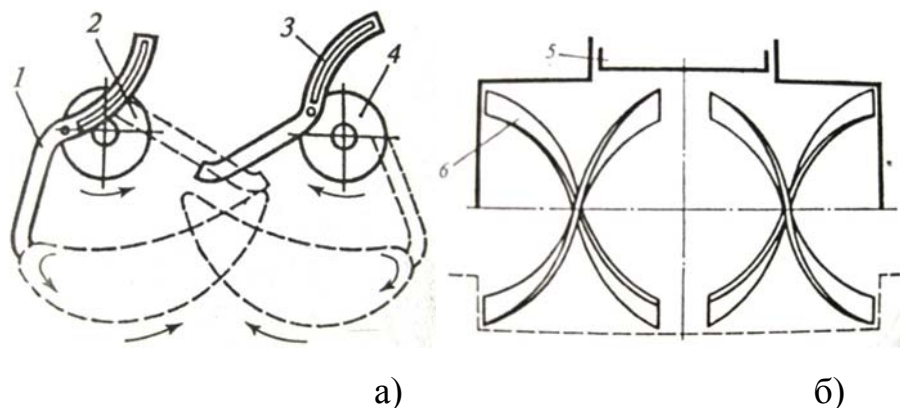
Рабочие органы снегопогрузчиков: а – лапового типа; б – фрезерного типа
